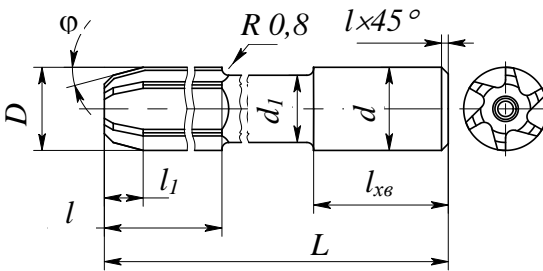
Розвертка з циліндричним хвостовиком
